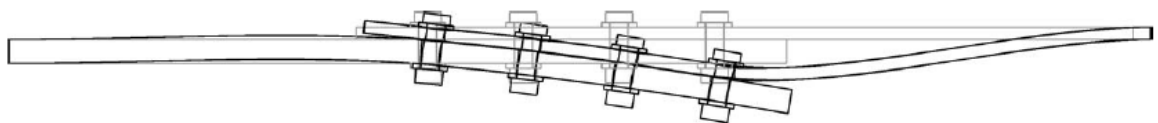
Déplacement hors-plan d'un assemblage simple recouvrement sollicité en cisaillement
